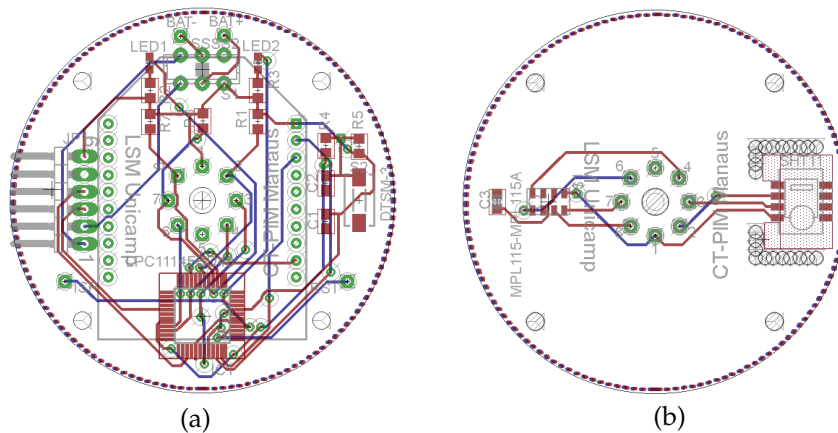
Leiaute da placa principal do nó (a) e da placa de sensores (b) do 3º protótipo.
